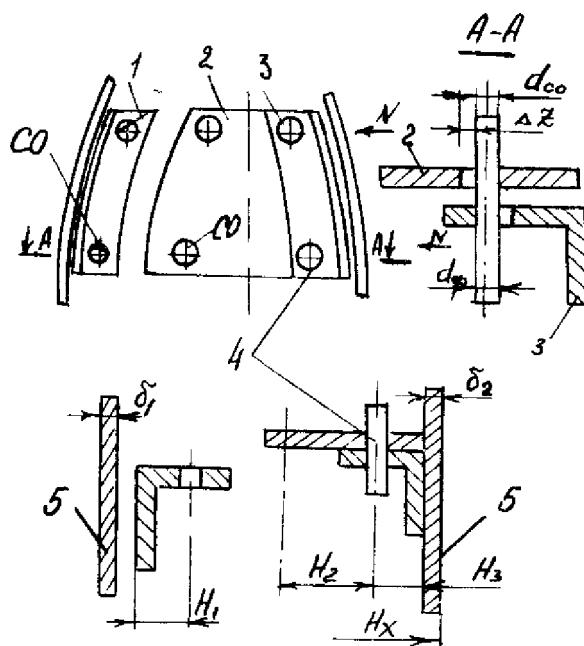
Сборка плоского каркасного узла по сборочным отверстиям: 1,3 — профили; 2 — стенка; 4 — фиксатор; 5 — обшивка
